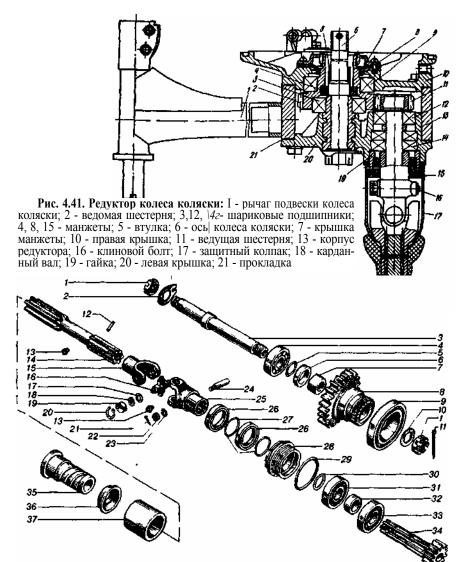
Редуктор с торсионным валом мотоциклов "Днепр-11/16": I, 22 - гайки; 2 - шайба специальная; 3 - ось коляски; 4, 9, 19, 31, 33 - подшипники; 5, 27 - пружины сальников; 6, 26 - манжеты сальников; 7 - втулка; 8 - шестерня ведомая; 10 - отражатель; 11, 21 - шплинты; 12 - штифт, 13 - масленка; 14 - вал карданный; 15 - вилка кардана; 16 - крестовина кардана; 17 - кольцо кардана; 18 - обойма кольца; 20 - кольцо замковое; 23 - шайба; 24 - болт клиновой; 25 - вилка кардана; 28 - гайка редуктора; 29 - кольцо; 30 - шайба регулировочная; 32 - втулка распорная; 34 - шестерня малая; 35, 36 - уплотнители; 37 - колпак кардана
